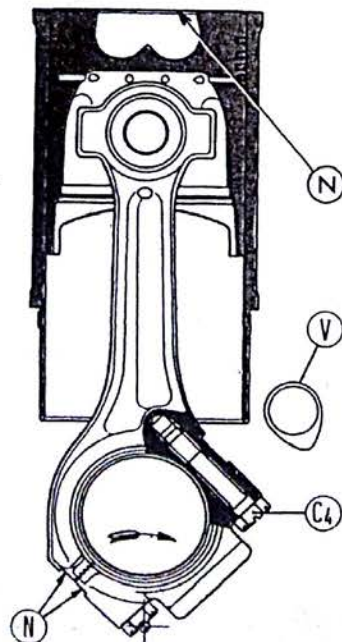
/39 - Vue en coupe de l'ensemble bielle piston.
